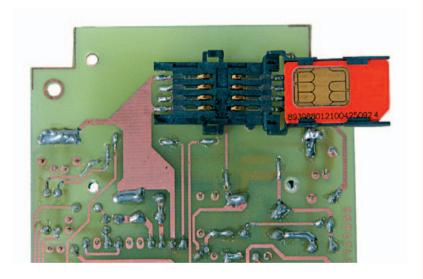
Photos d'un des prototypes de la platine du téléphone fixe-GSM, face soudures, où est monté le porte-SIM (ci-dessus: détail).
